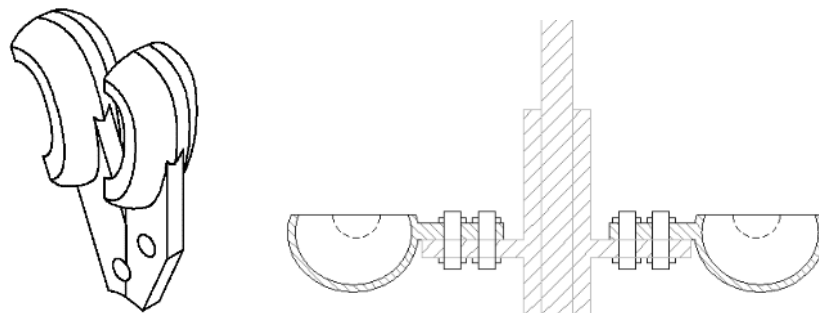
Diseño final álabes turbina Turgo según dimensiones calculadas.
